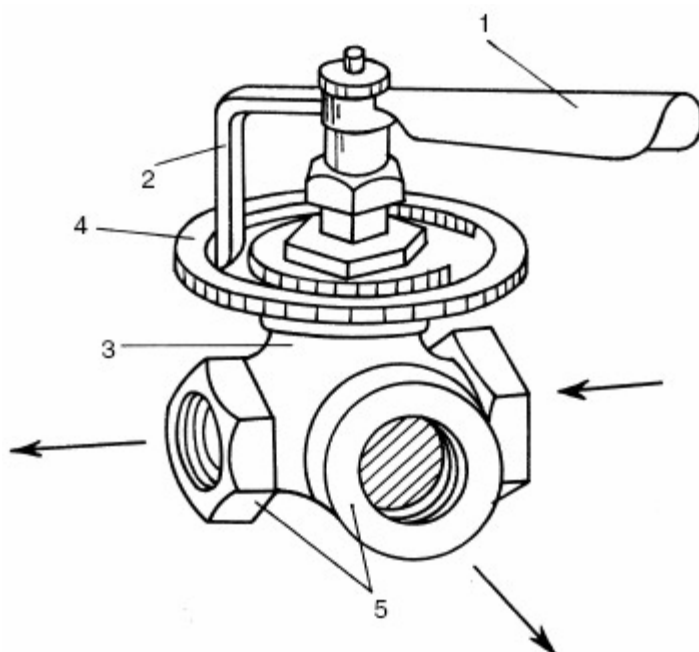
Трехходовый кран: 1 – рукоятка; 2 – упорный палец; 3 – корпус; 4 – розетка; 5 – проходы корпуса
